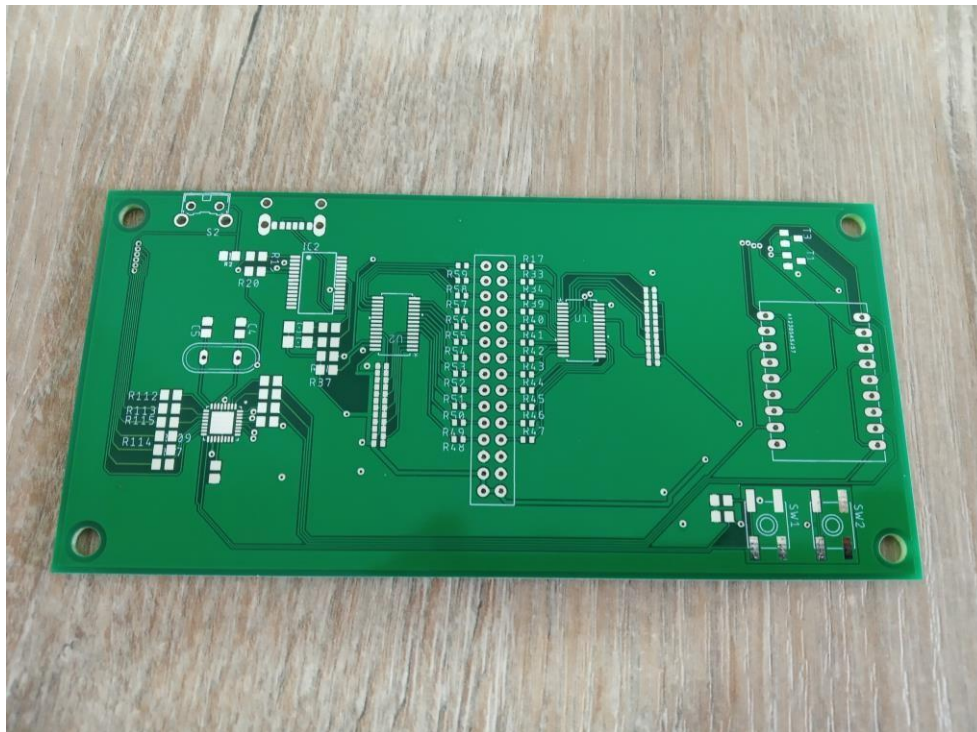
Tarjeta PCB de control AC Y DC sin componentes. Tobón. (2019)
